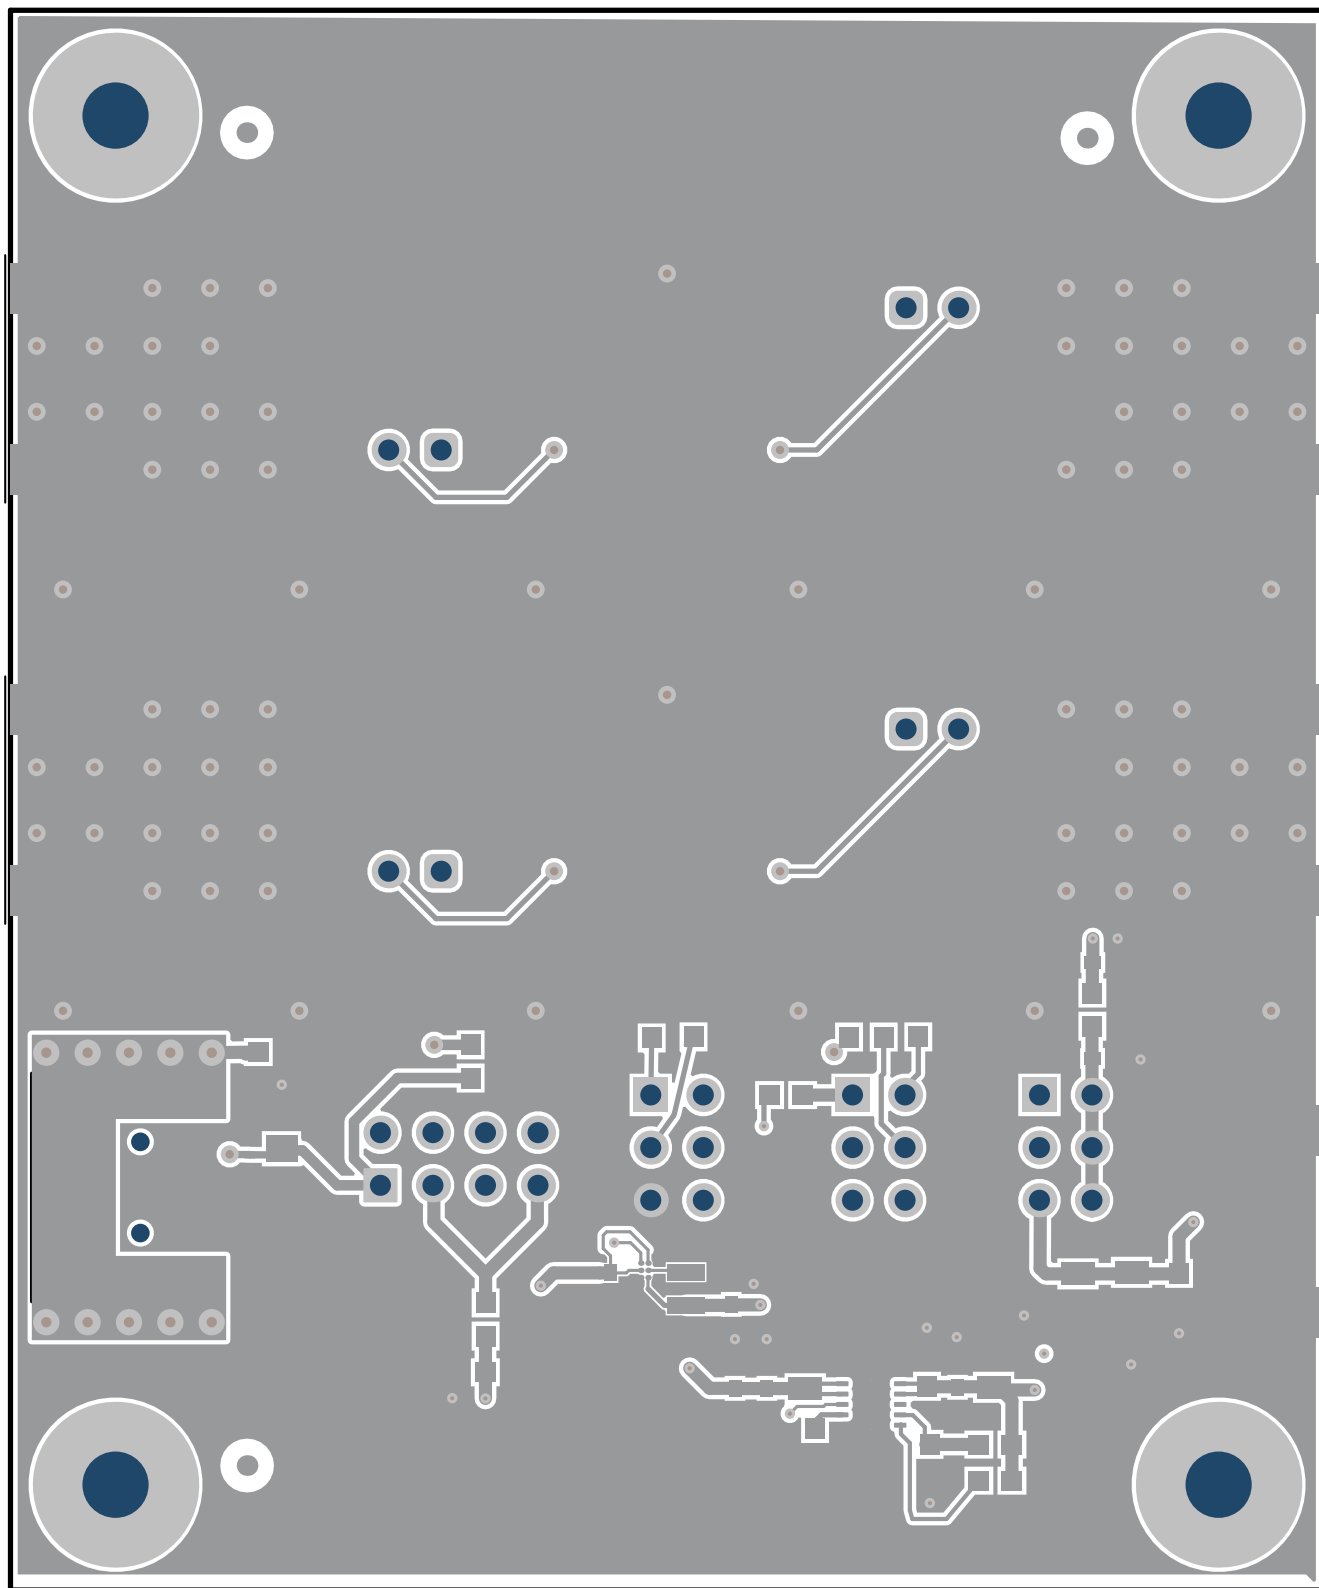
CDC6 EVM の PCB レイアウト例 — 最下層
